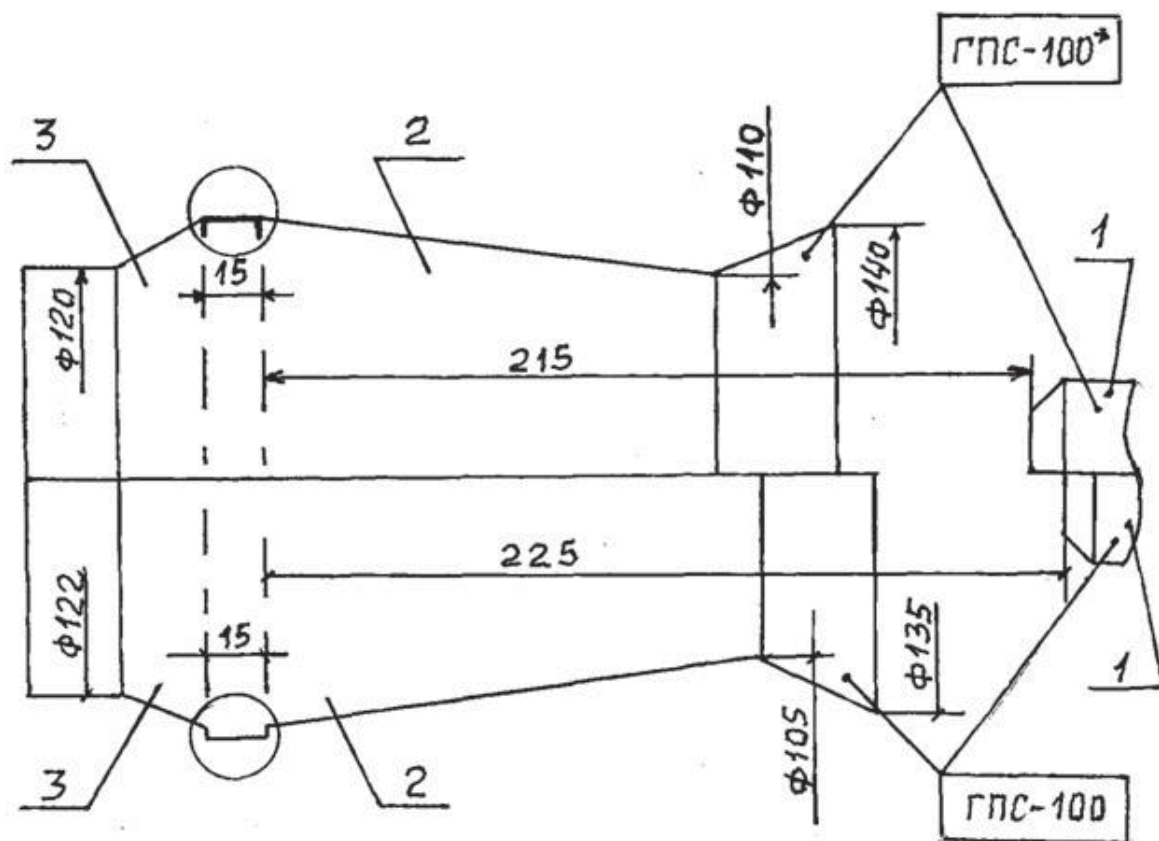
Конструктивные размеры корпуса генераторов ГПС-100* и ГПС-100:
